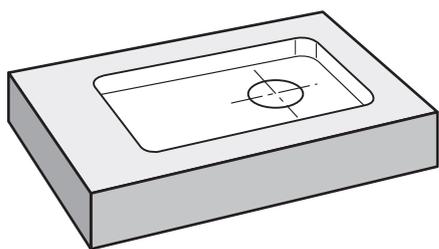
Exemple de pièce – Usinage d'un ajustement
